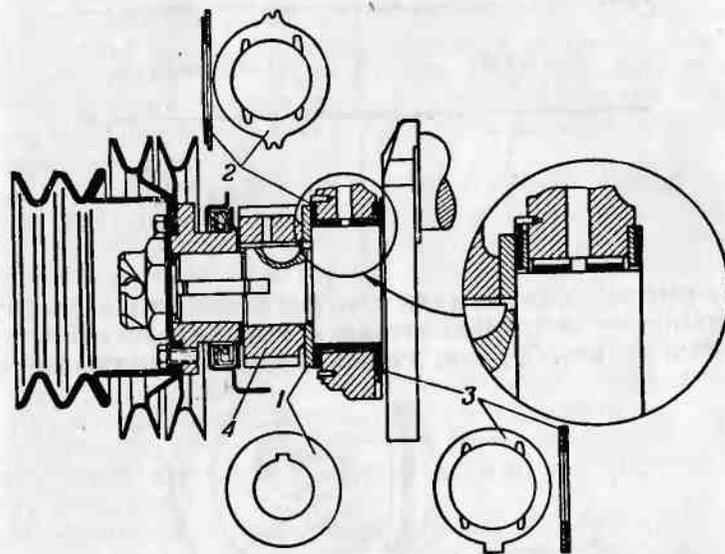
Передний подшипник коленчатого вала двигателя с упорными шайбами:
